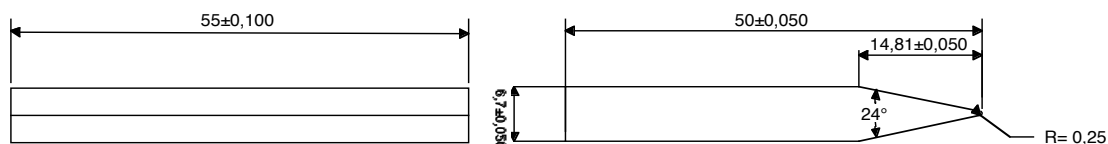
Eprouvette longue de fatigue thermique type FT-L.
